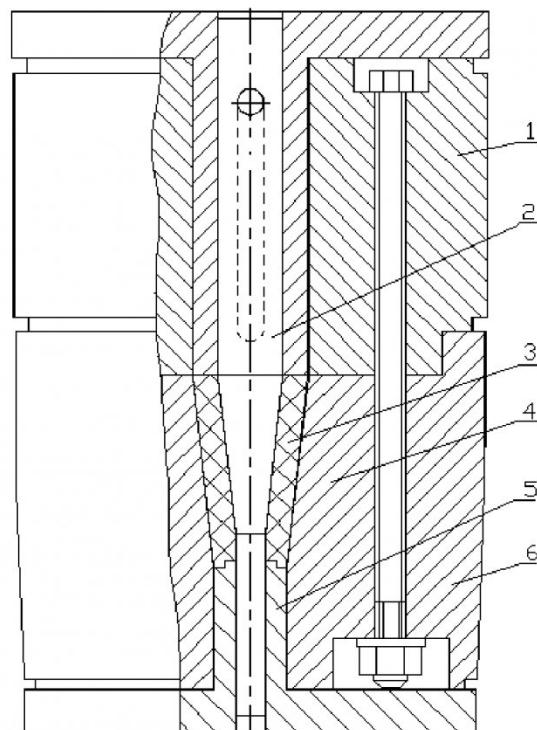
Схема двухстороннего прессования сопел: 1 - верхняя пресс-форма; 2 - верхний пuhanсон-стержень; 3 - заготовка (твёрдосплавная смесь); 4 - матрица; 5 - нижний пuhanсон-стержень; 6 - нижняя пресс-форма.
